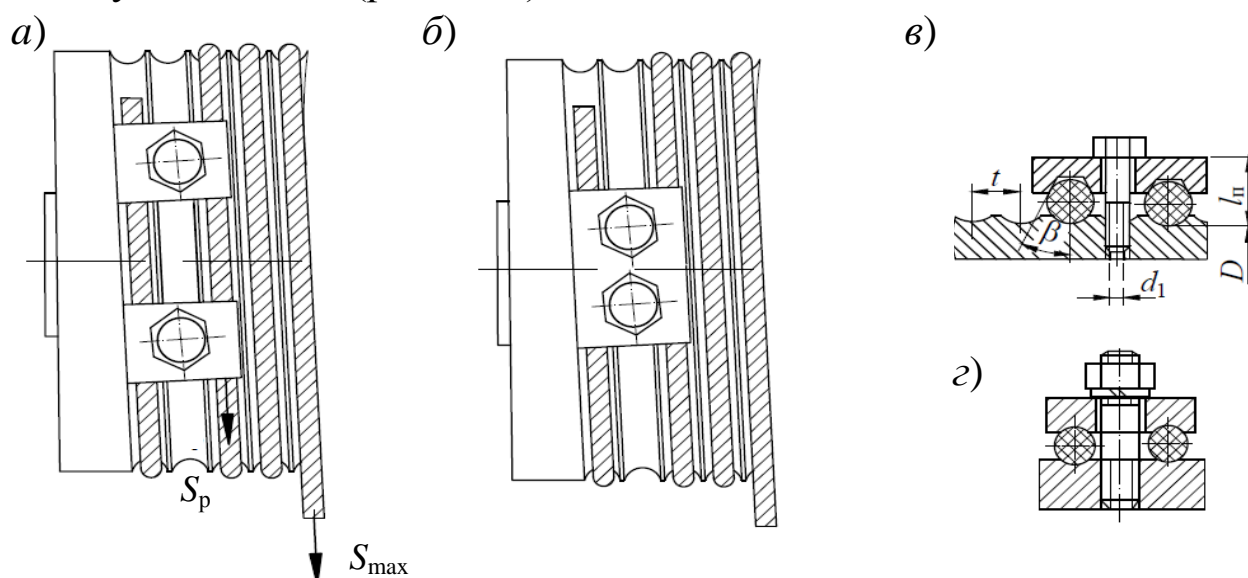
Крепление каната на барабане: а – одноболтовыми накладками; б – двухболтовыми накладками; в – накладка с трапецидальными канавками; г – накладка с полукруглыми канавками
